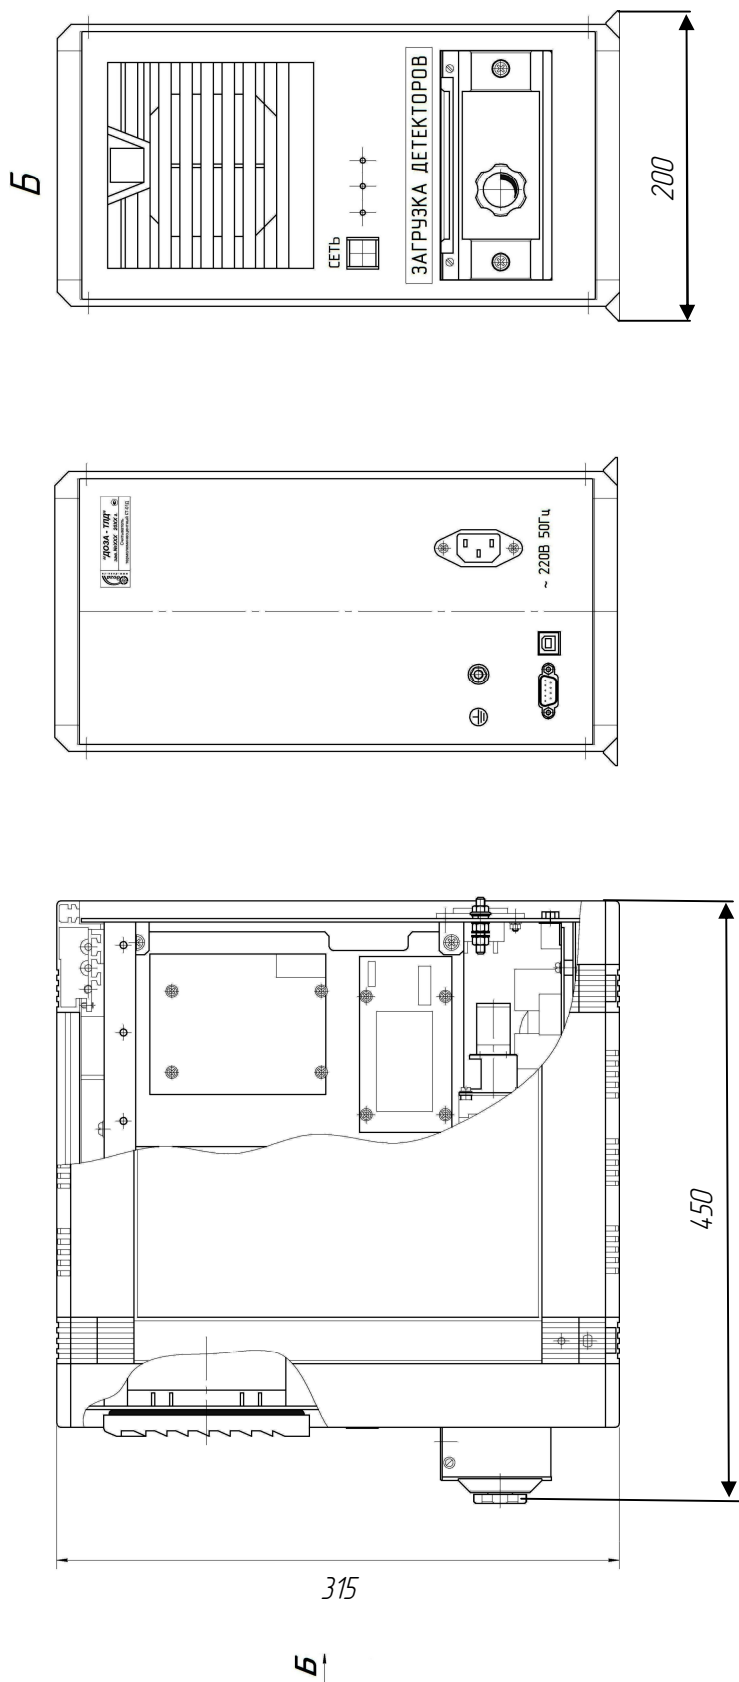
Считыватель термолюминесцентный СТ-01Д ФВКМ.468169.004
